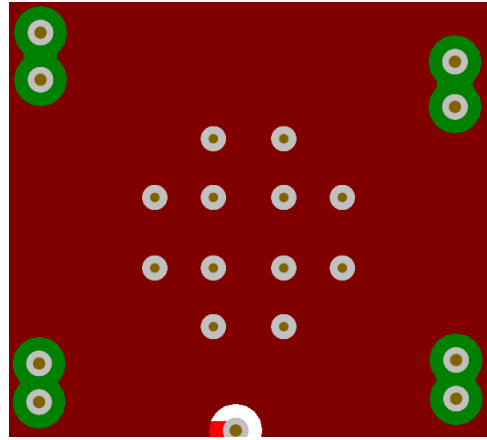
LMK1D2106L 的 PCB 布局示例，GND 层
